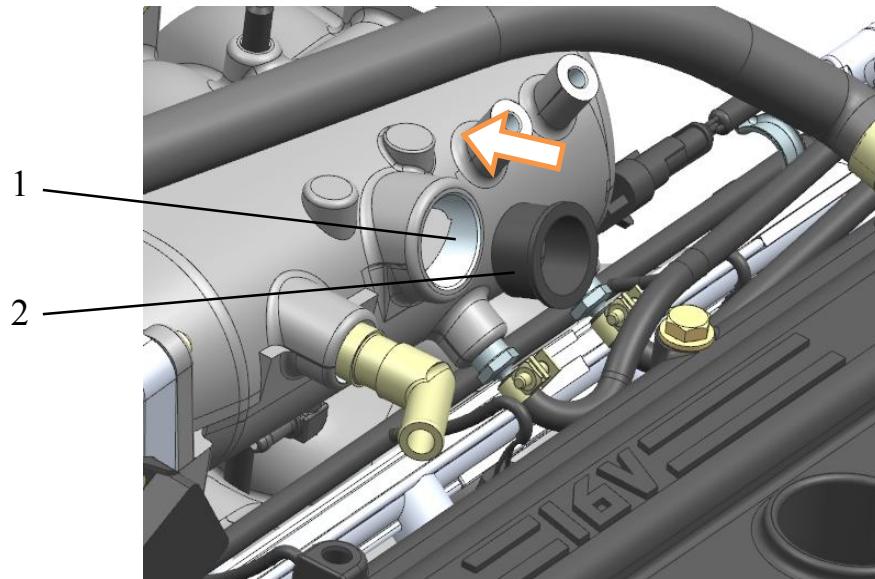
Установка уплотнительного кольца патрубка регулятора холостого хода:
